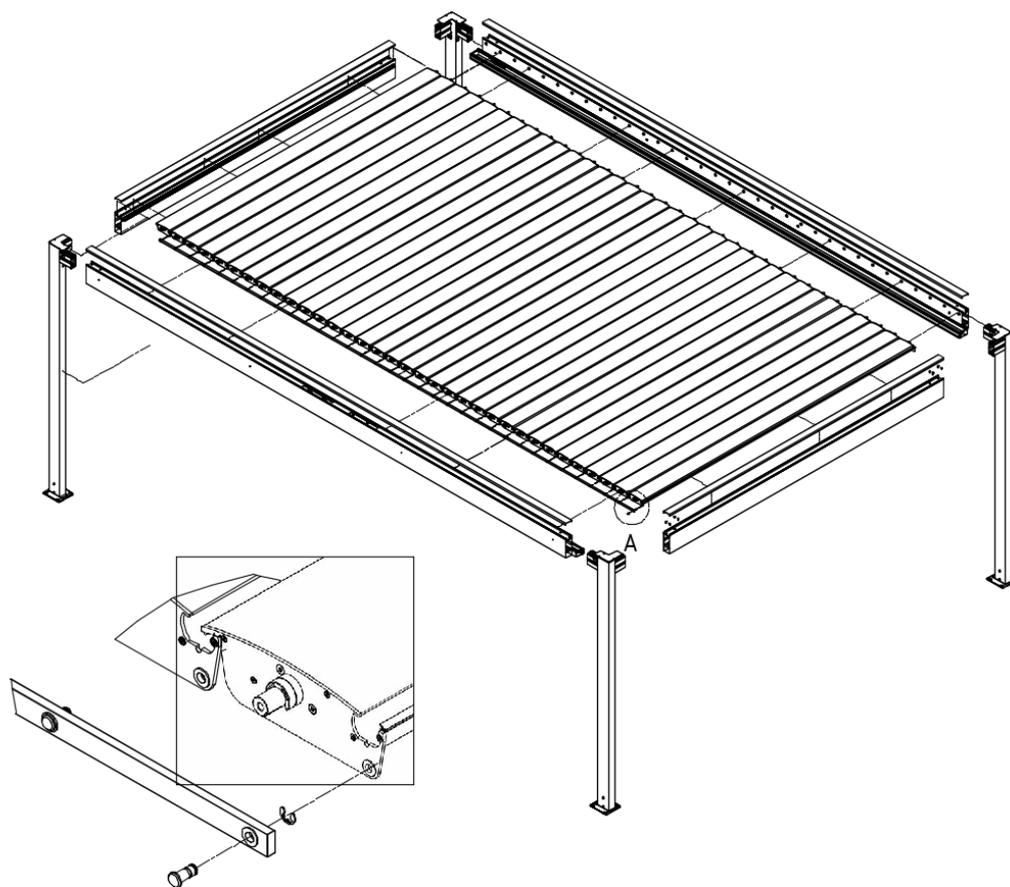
Vue de l'assemblage des éléments de la Pergola SB 400PRO autoportante
